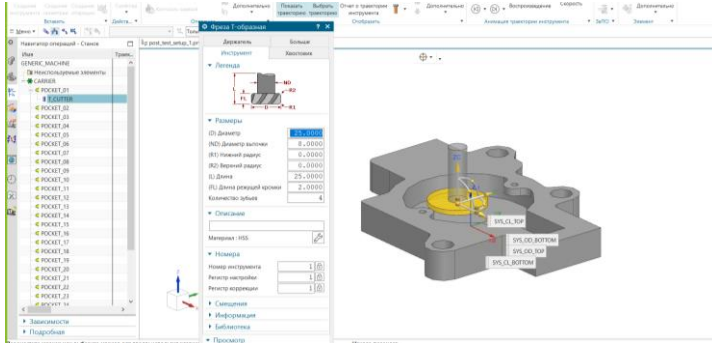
Параметри Т – подібної фрези Обробка поднутрений
